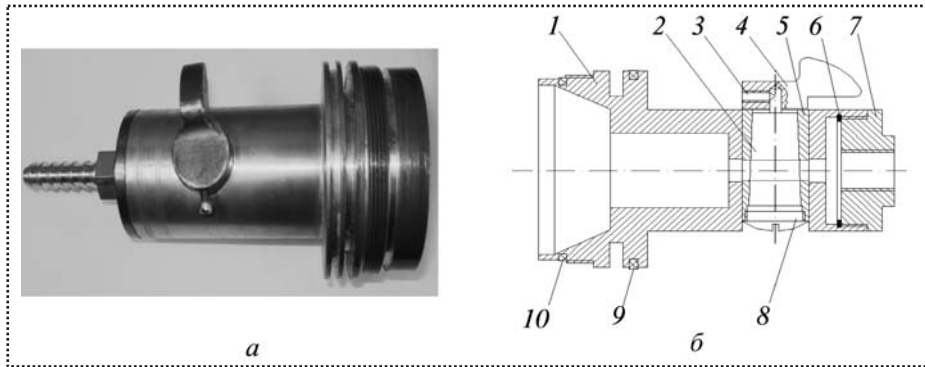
Общий вид (а) и конструкция (б) входного устройства
